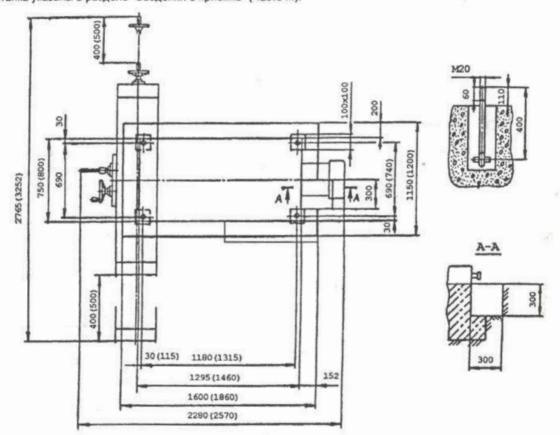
Установочный чертеж станков (в скобках даны размеры для 6Т83Ш)
